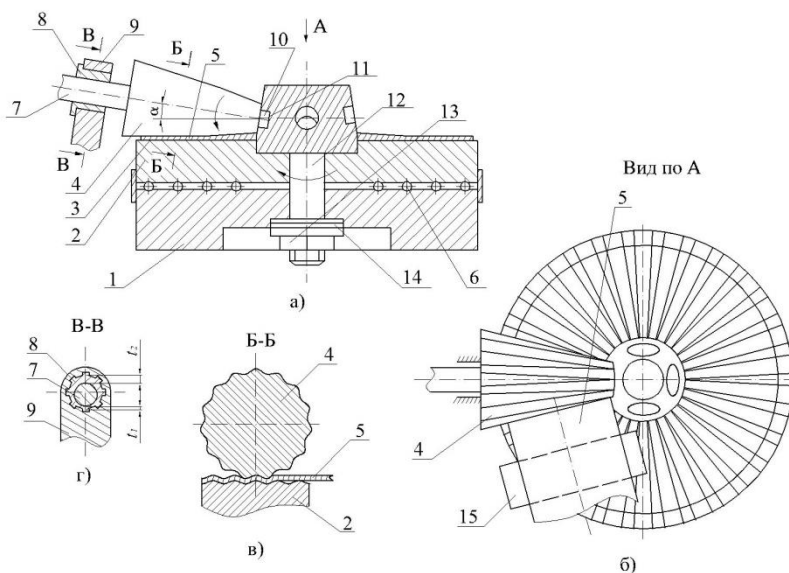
Пристрій для виготовлення гофрованих гвинтових заготовок: а) загальний вигляд; б) вид по А; в) січення по Б-Б; г) січення по В-В
